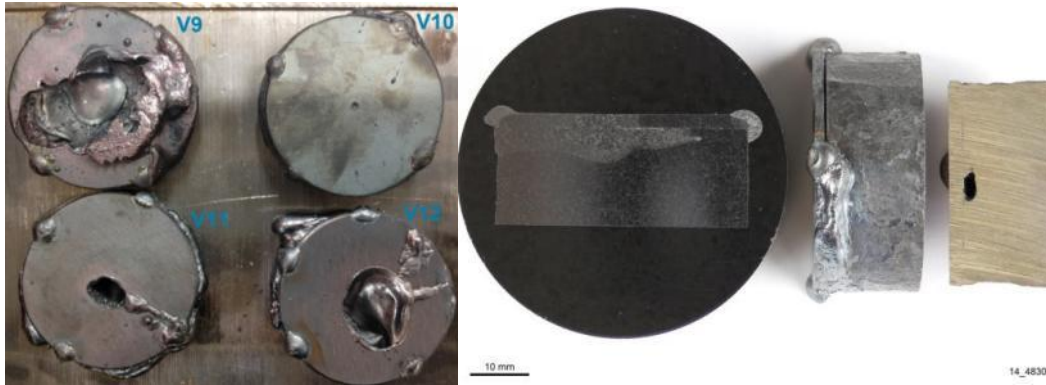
links: Übersicht der elektronenstrahlgeschweißten Proben V9 bis V12, vertikale Anordnung; rechts: makroskopische Aufnahme des Querschliffes und der Probenstücke, Probe V14
